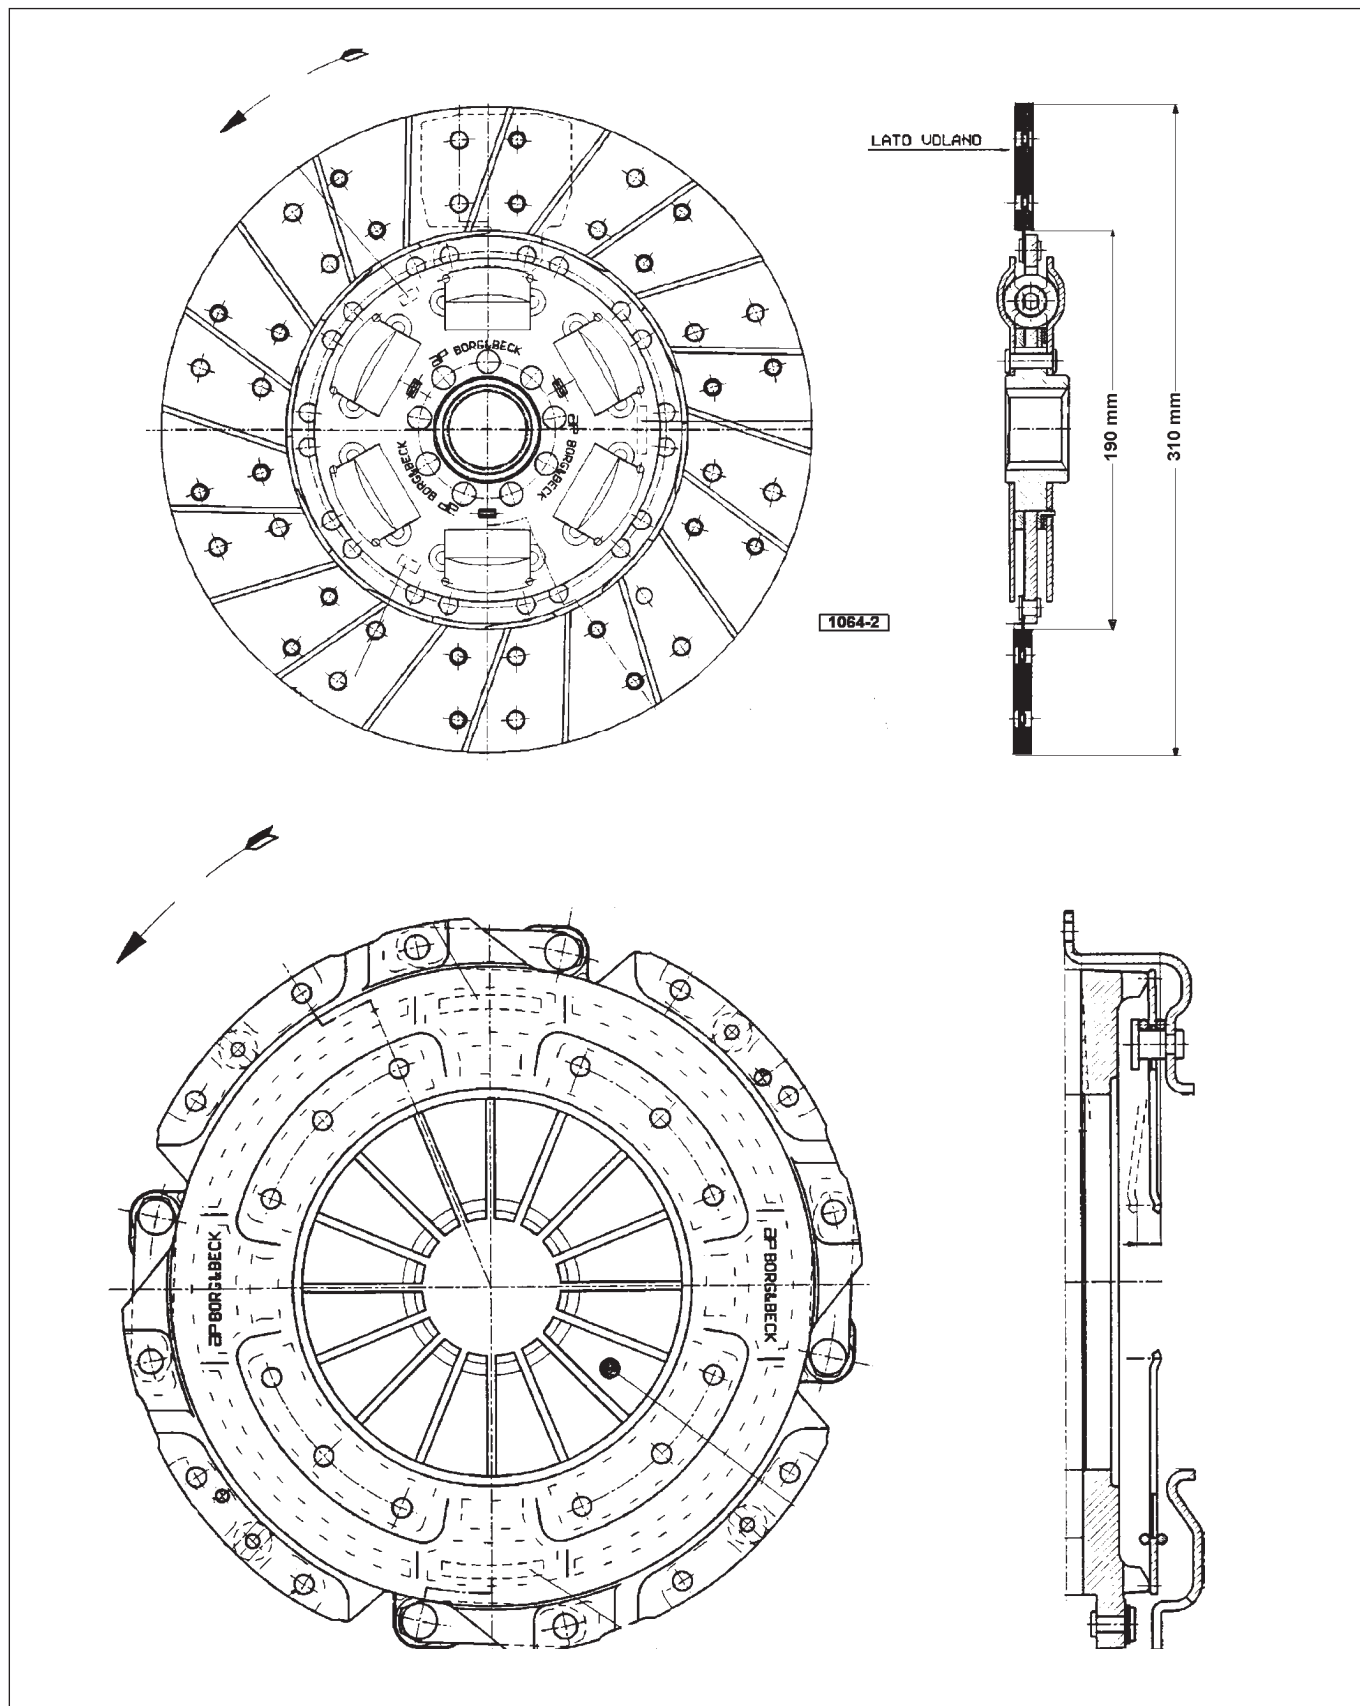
Vue d'ensemble de l'embrayage 70F4 - F80 - F90.
